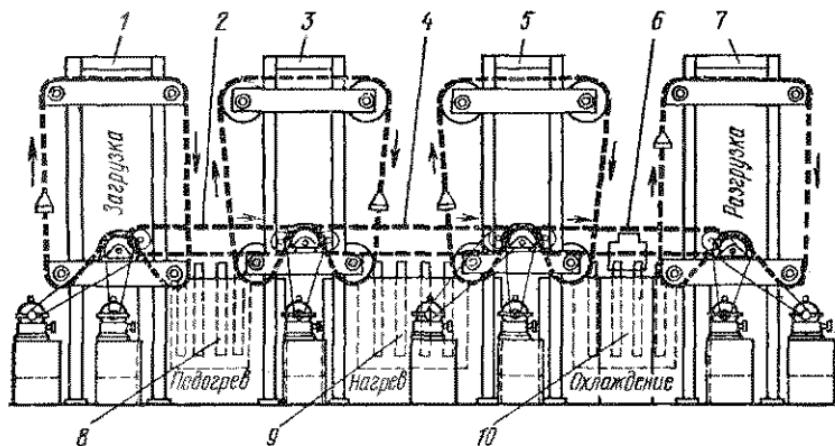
Схема конвейерного агрегата для закалки инструмента из быстрорежущей стали:
